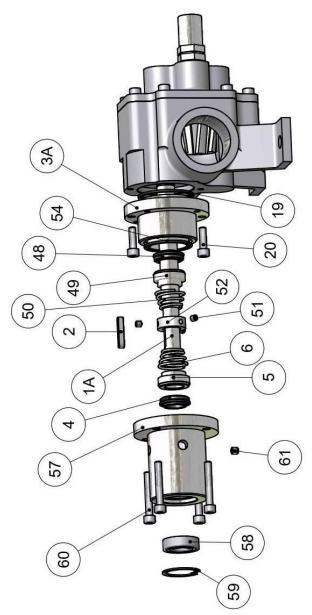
Tenuta Doppia Back-to-Back Figure 2 - Double Back-to-Back Seals
